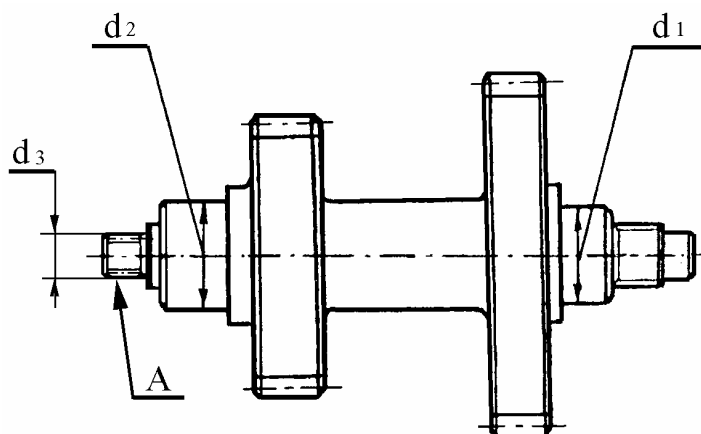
Вал промежуточный 2121-1802084-10, 2121-1802084-20, 21213-1802084-10:
